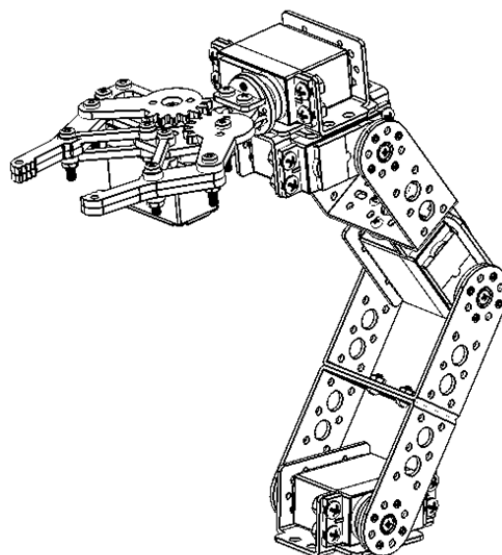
Внешний вид части руки манипулятора «механическая рука».
